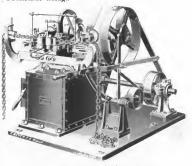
Elektrische Kettenschweissmaschine.
